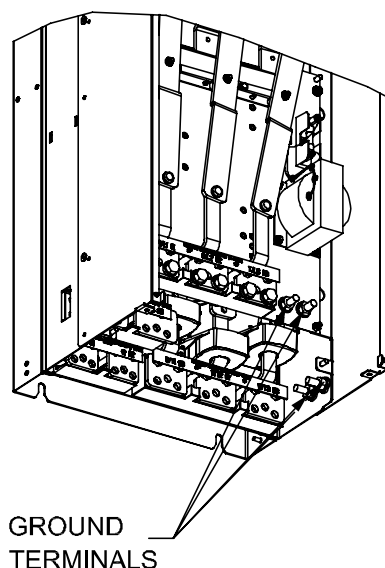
Расположение клемм заземления IP00, размер стойки D
